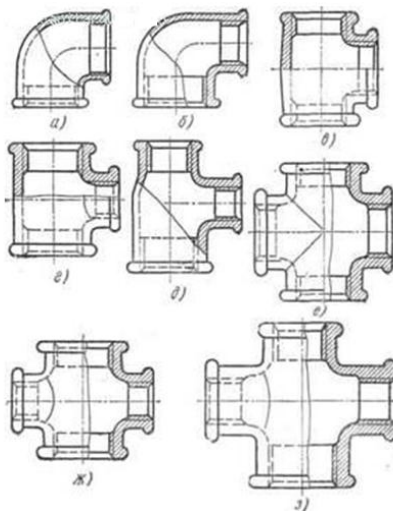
Соединительные части из ковкого чугуна для соединения труб под углом и устройства ответвлений [10]:
